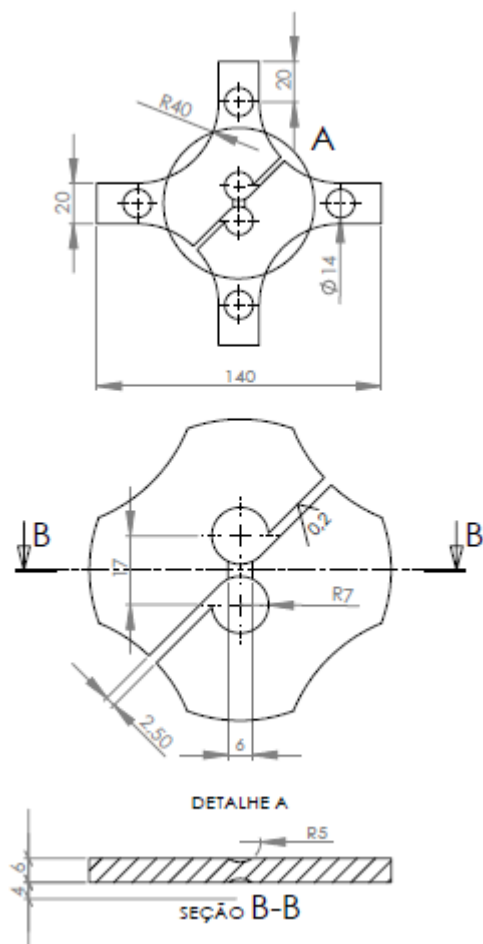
Dimensões do corpo de prova de Arcan modificado
